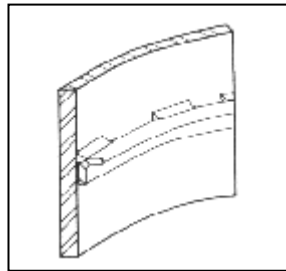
Soporte de bandeja, cordones de soldadura discontinuos - soporte adecuado, corrosión severa
